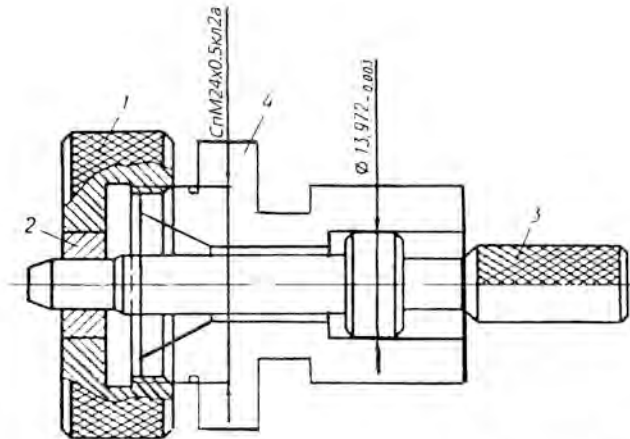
Калибр положения для контроля биения поверхностей оправы
